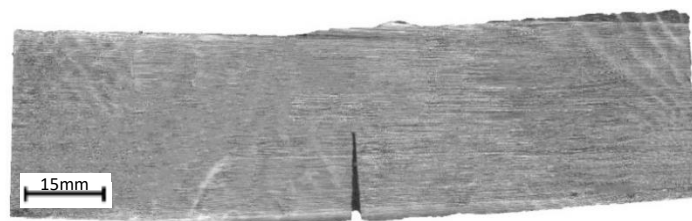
Distorção no corpo de prova da soldagem filetada. Fenômeno similar aconteceu em todas os conjuntos soldados.
